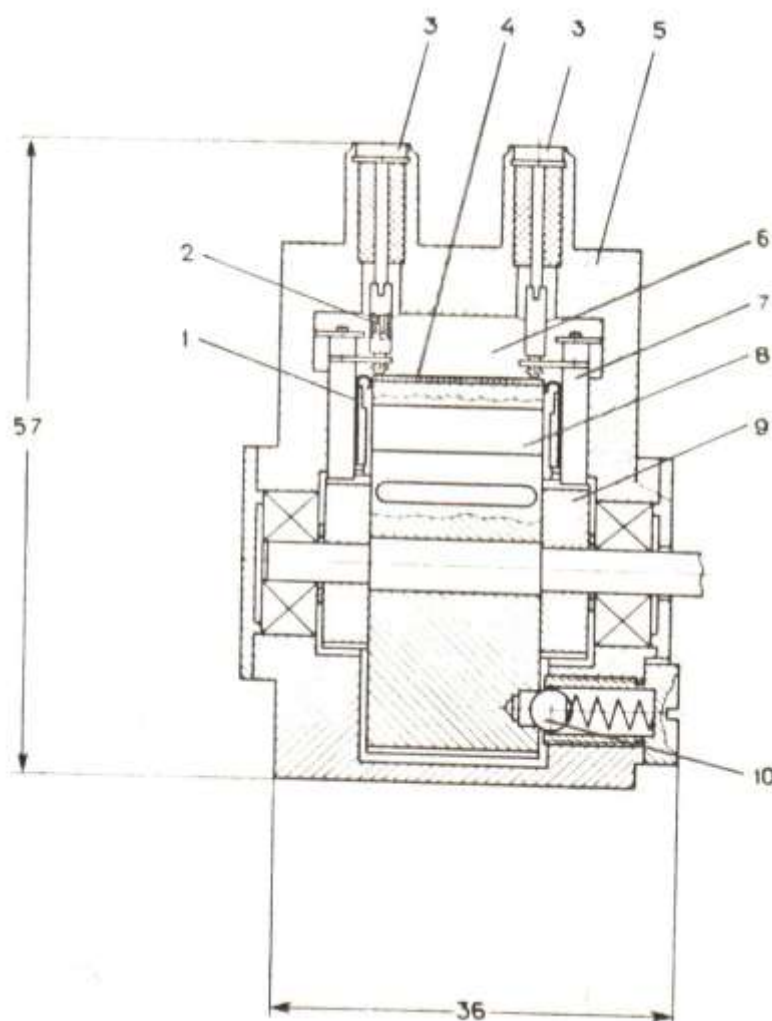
Упрощенный чертёж малогабаритного ступенчатого аттенюатора в разрезе
